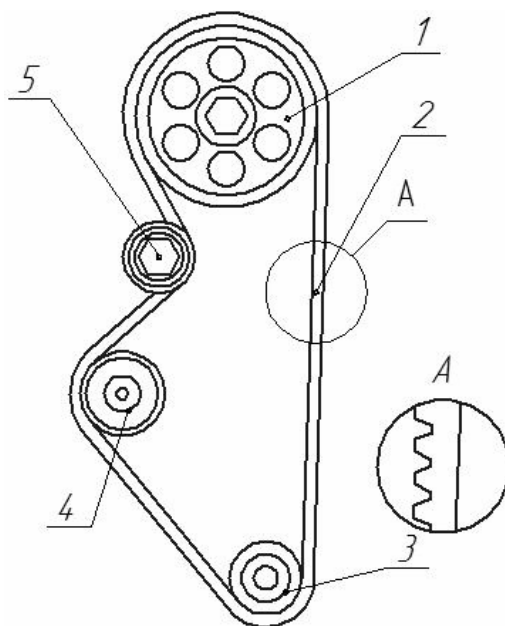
Регулировка натяжения ремня привода ГРМ на автомобиле ВАЗ-2108:
